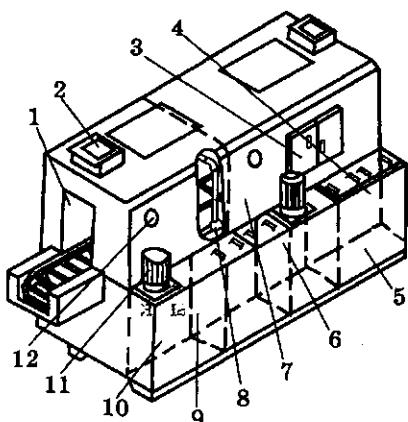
Машина для струйной очистки деталей: 1 — тамбур; 2 — вентиляционный отвод; 3 — люк; 4 — флотационный отсек; 5 и 9 — фильтры напорные; 6 — ванна с раствором и нагревательными элементами; 7 — очистная камера; 8 — система гидрантов; 10 — емкость подачи раствора; 11 — насосный агрегат; 12 — приборы
